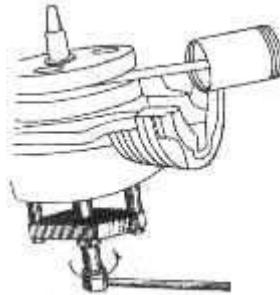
Выпрессовка коленчатого вала из левой половины картера силового агрегата
